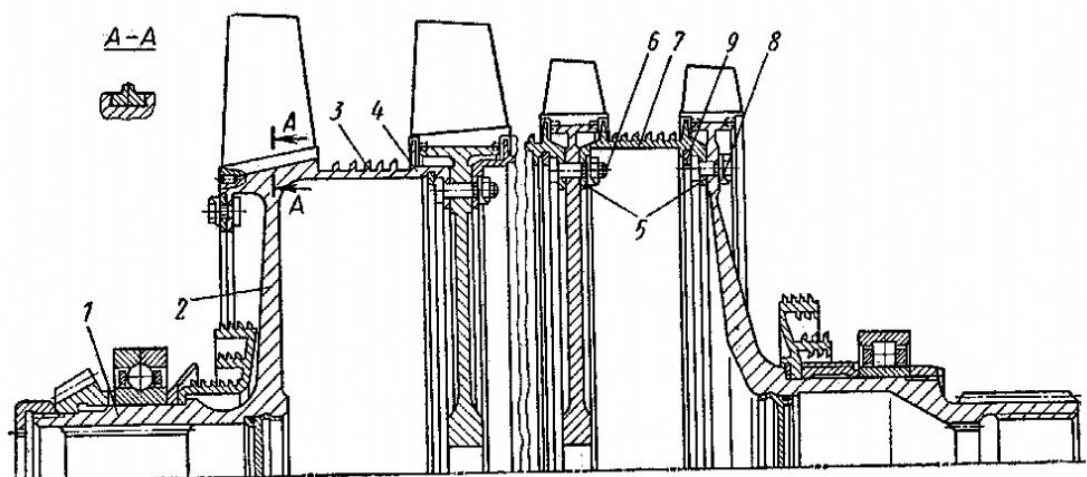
Ротор смешанного типа с креплением секций призонным болтами:
